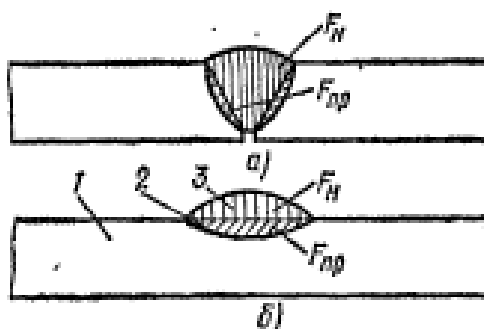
2 – Сечение сварного шва без разделки кромок
